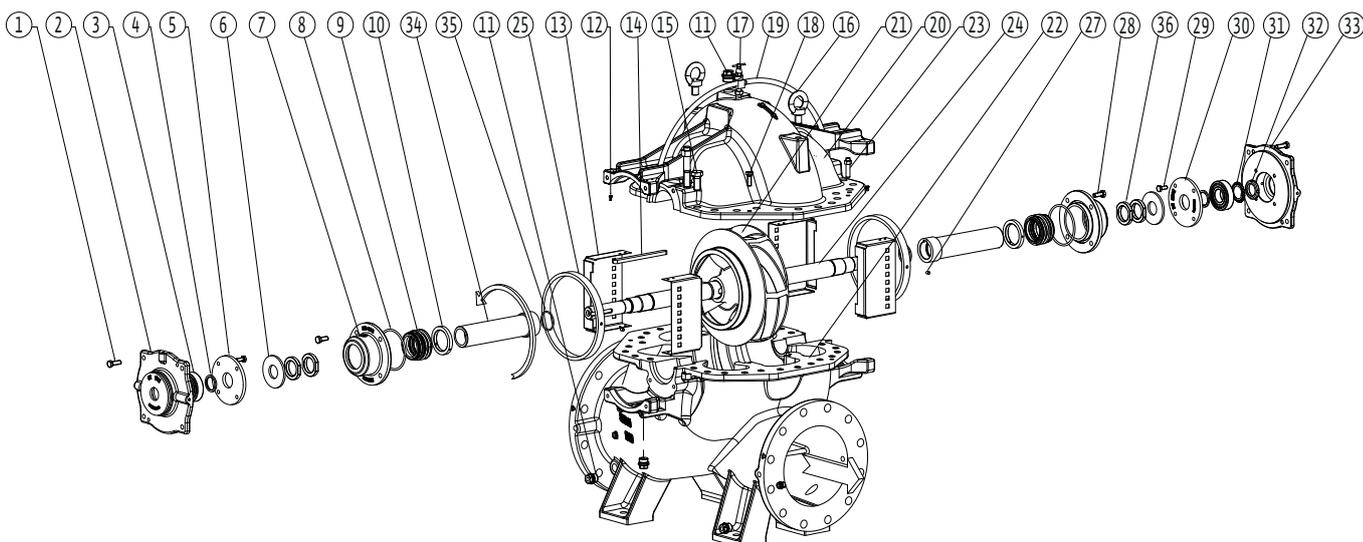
Explosionsansicht der Atmos TERA-SCH-Hydraulik (Ausführung mit Gleitringdichtung mit Hülzen)
